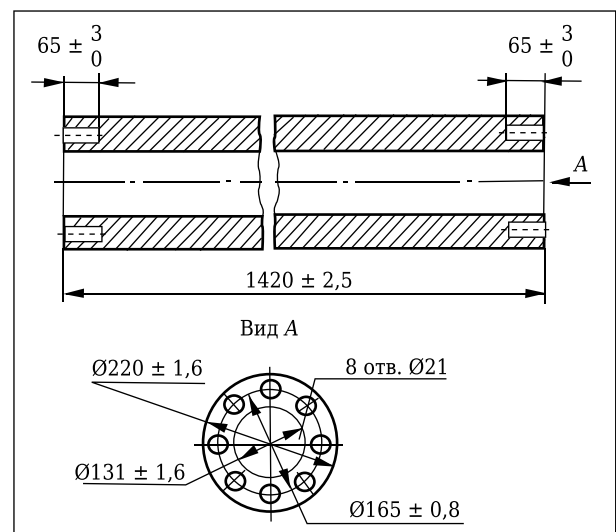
Кварцевая оболочка ролика для транспортировки стальной ленты в печах обжига динамной стали
